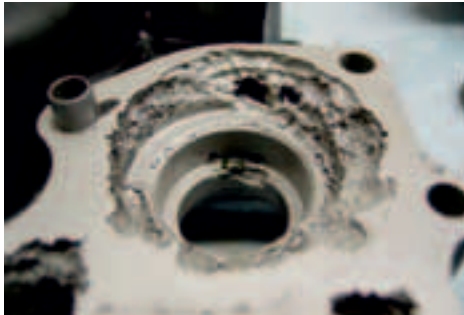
Galvanische Korrosion am Wasserpumpengehäuse
